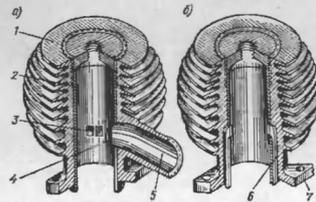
Цилиндр двигателя Д5: а — разрез по выходному патрубку; б — разрез по продувочным окнам:
